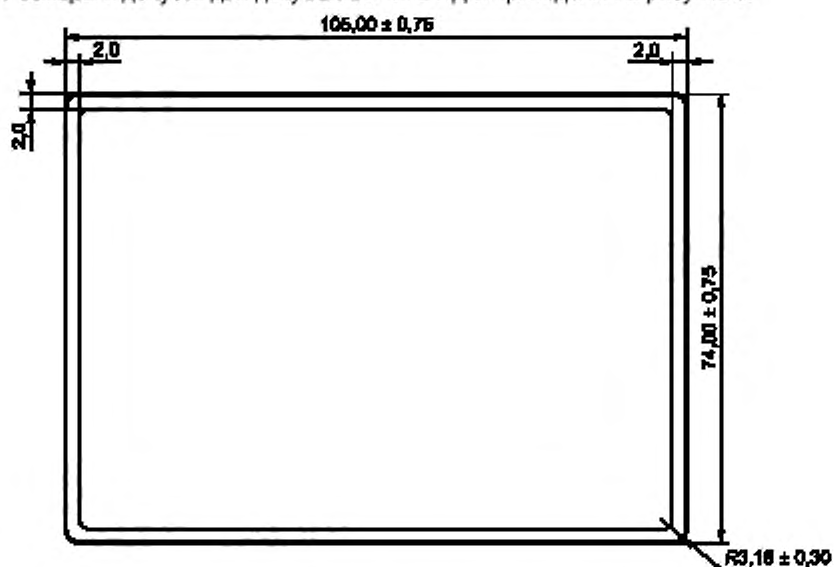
Размеры и допуски документа ПД-2
